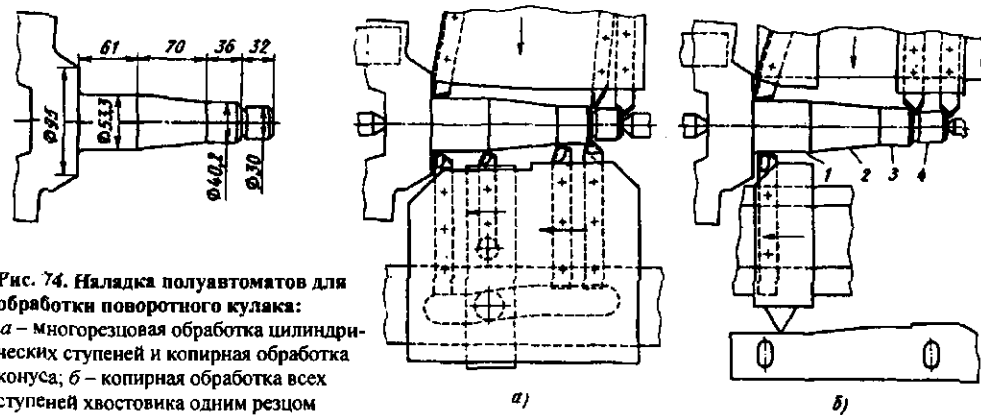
Наладка полуавтоматов для обработки поворотного кулака: а – многорезцовая обработка цилиндрических ступеней и копирная обработка конуса; б – копирная обработка всех ступеней хвостовика одним резцом
